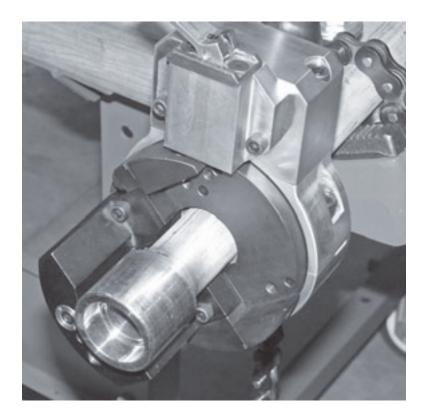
La photo représente le porte-outil de coupe axiale d'emboîtement en position pour la coupe d'emboîtement de soudure.
